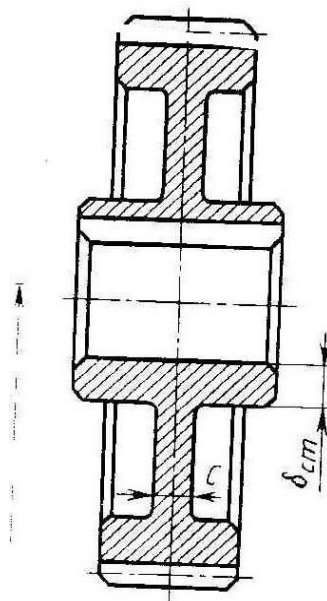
4 – Параметры зубчатого цилиндрического колеса.
